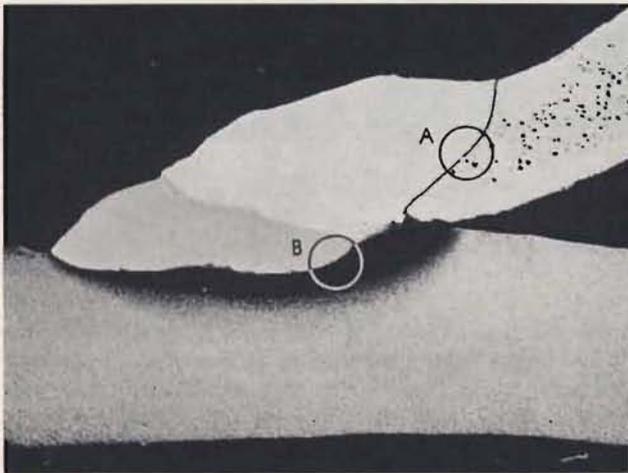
Makroschliff einer Schweißverbindung (x 10)
